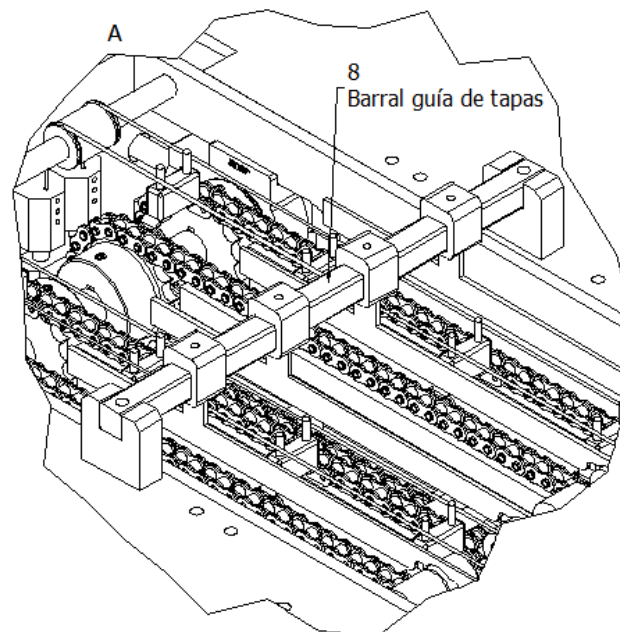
DETALLE BARRAL GUÍAS
